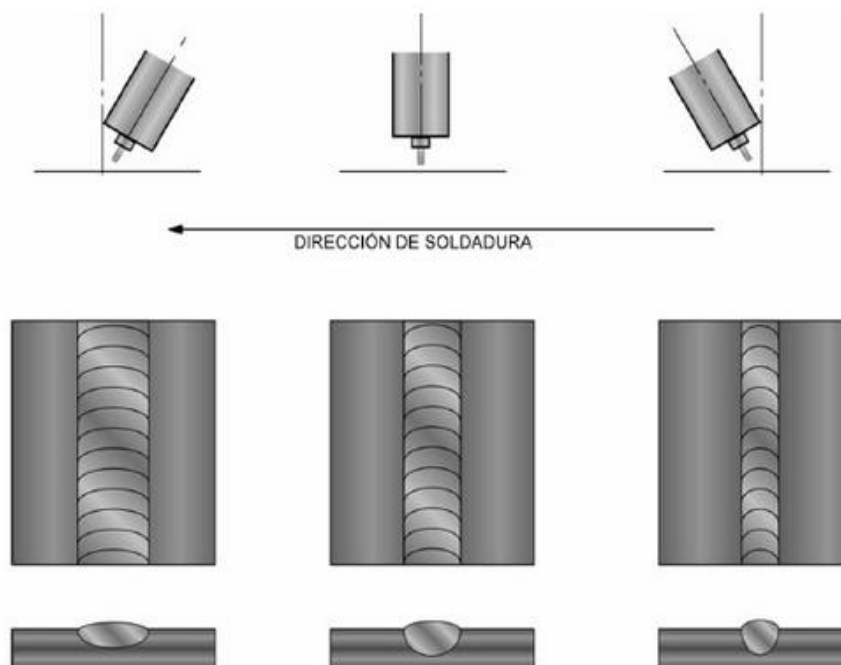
6: Efecto de la posición del electrodo y de la técnica de soldadura.
